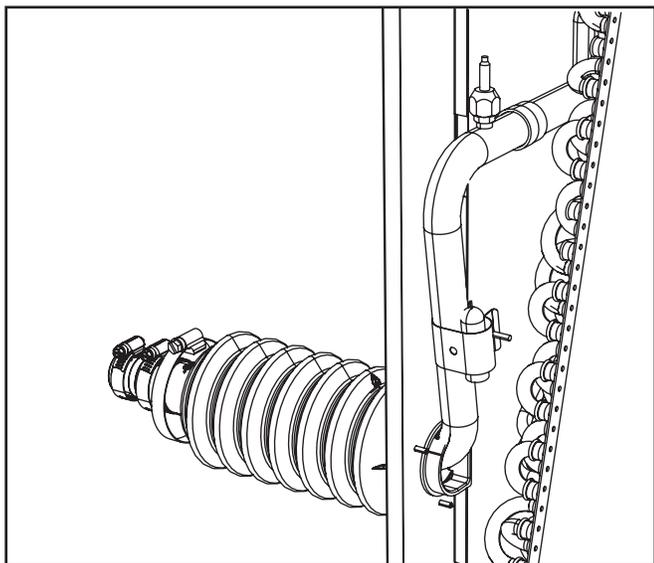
Conduite d'aspiration du CK40CT49C-60C avec manchon de connexion du jeu de conduites
